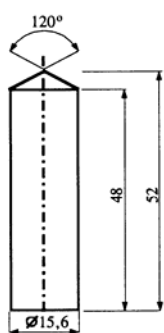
Цилиндрический бронзовый поршень; размеры в мм
